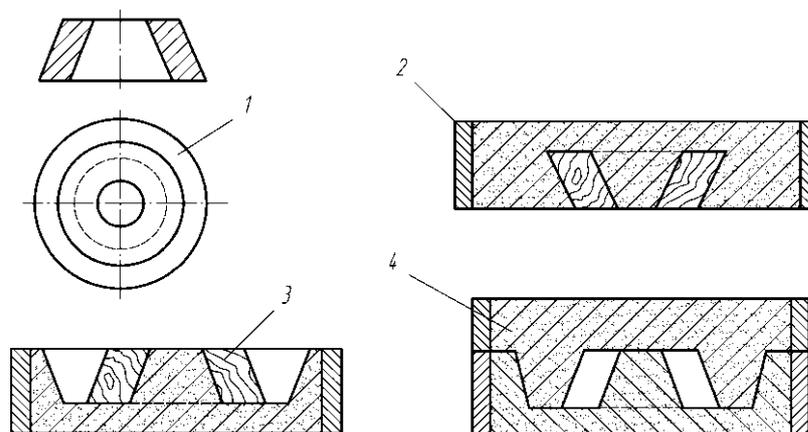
Схема этапов формовки с подрезкой: 1 - отливка; 2 - набивка нижней опоки; 3 - подрезка вокруг модели; 4 - собранная форма
